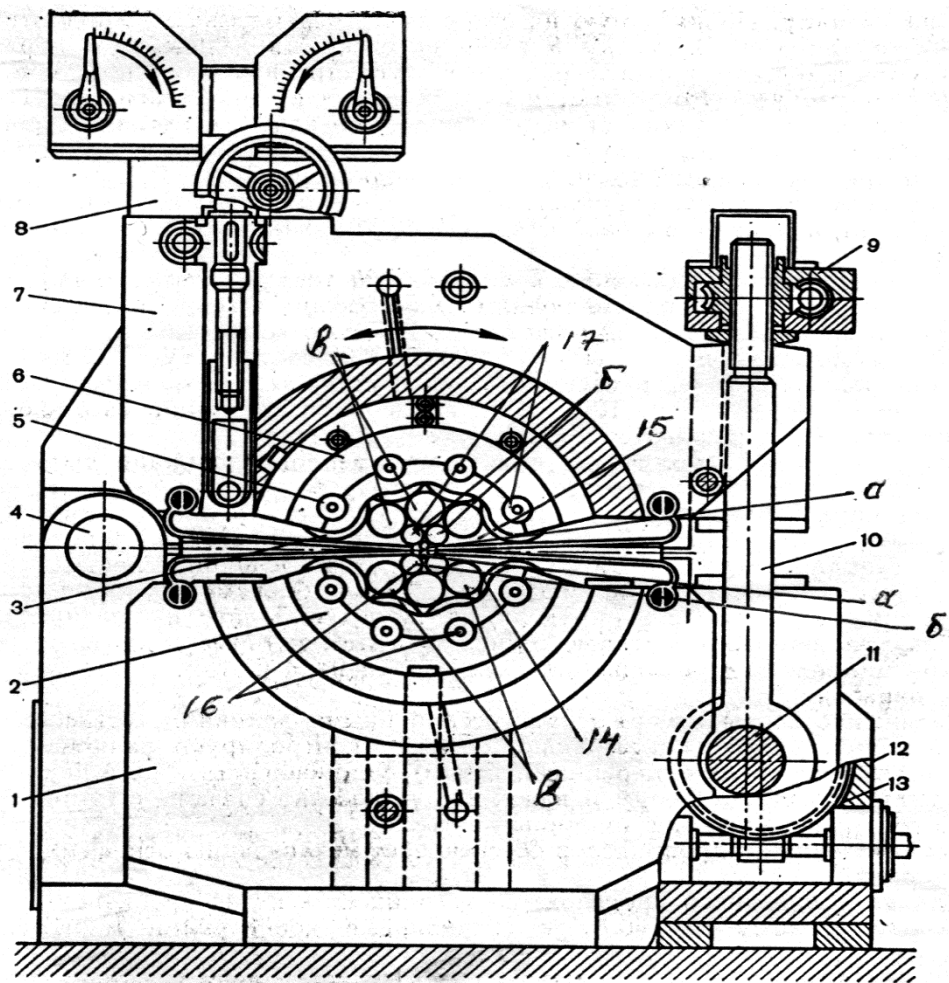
Дванадцятивалкова кліть Рона фірми "Sundwiq" :1 – нижня частина станини, 2 – нижня касета валків, 3 – підшипник опорний, 4 – шарнір, 5 – вісь, 6 – верхня касета валків, 7 – верхня частина станини, 8 – механізм регулювання профілю валків, 9 – установлюючий редуктор, 10 – тяга, 11 – ексцентриковий вал, 12 – натискний механізм, 13 – черв'ячний редуктор, 14 і 15 – відповідно виточки (напіввікна) у нижній та верхній половині станини, 16 і 17 – відповідно нижня та верхня 10-ти валкова піраміда.
